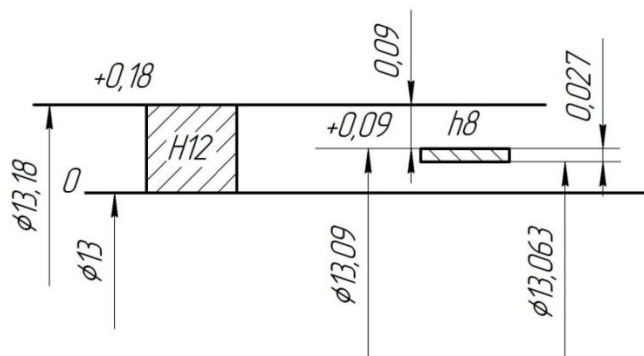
Схема полей допусков сверла и отверстия
